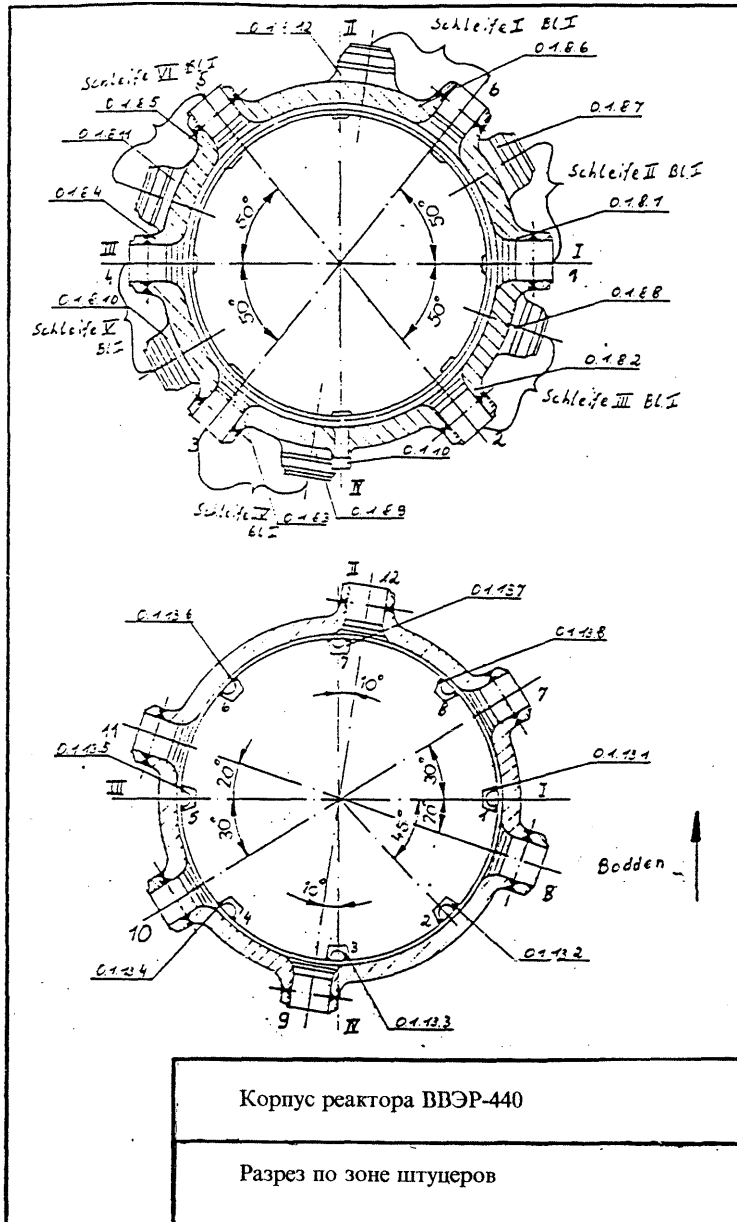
Поперечный разрез зоны патрубков, корпус ВВЭР-440; В-230
